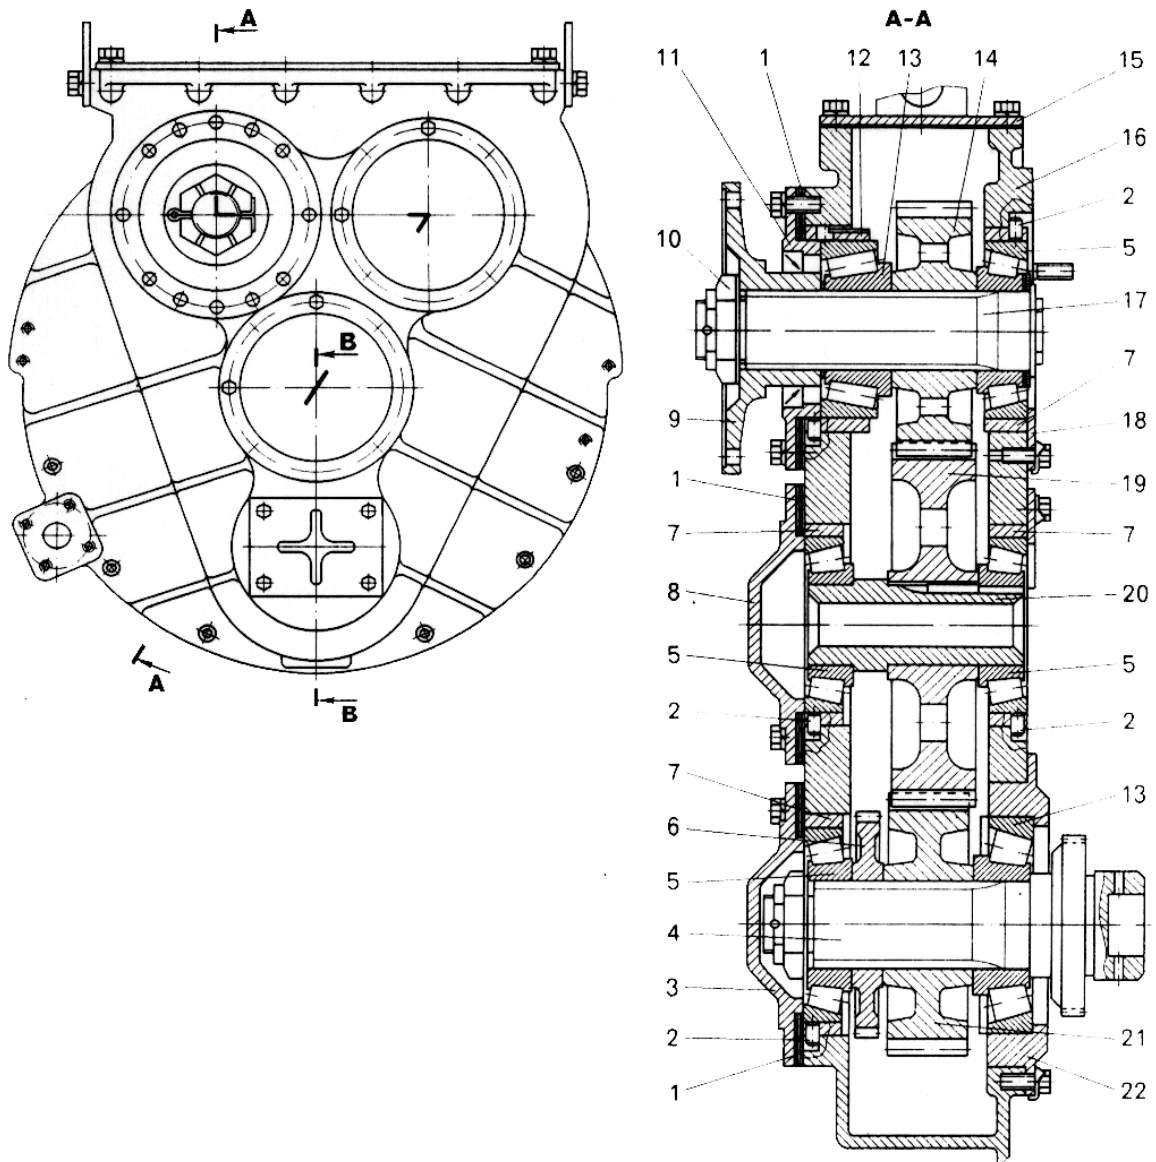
Согласующая передача: 1 – регулировочные прокладки, (разной толщины); 2 – штифты фиксаторы стаканов подшипников; 3 – крышка ведомого вала; 4 – ведомый (вторичный) вал; 5, 13 – роликовые радиально упорные подшипники; 6 – ведущая шестерня привода насоса; 7, 12 – стаканы подшипников; 8 – крышка промежуточного вала; 9 – фланец крепления карданного вала; 10 – прорезная гайка; 11 – крышка ведущего вала; 14 – ведущая шестерня; 15 – крышка картера; 16 – картер; 17 – ведущий (первичный) вал; 18 – прижимная пластина; 19 – промежуточная шестерня; 20 – промежуточный вал; 21 – ведомая шестерня; 22 – стакан
